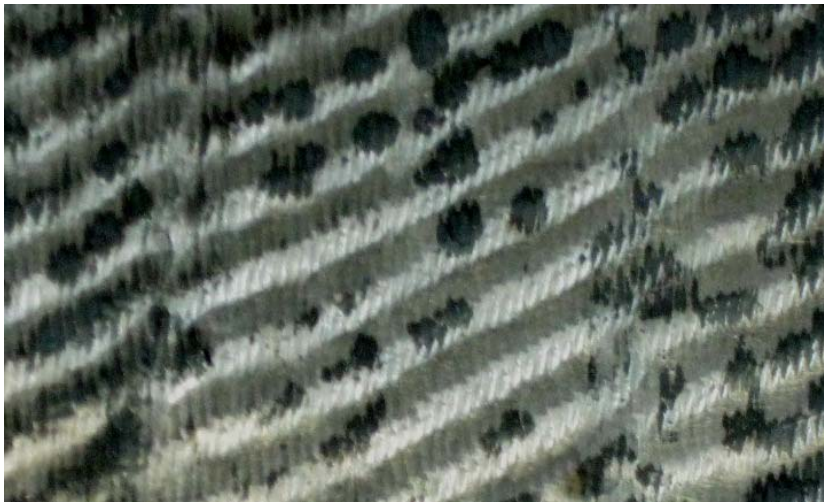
Поверхность втулки прессового инструмента после нескольких прессовок
